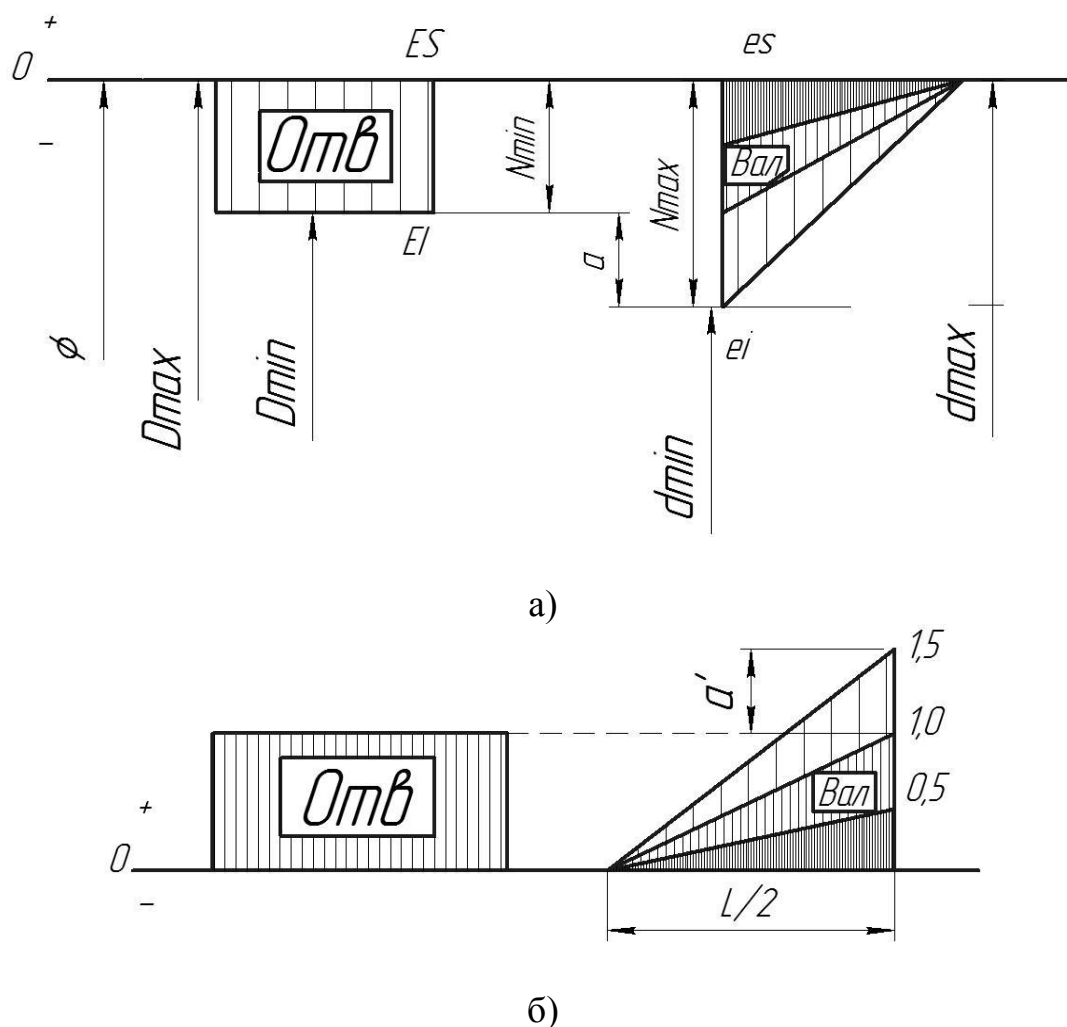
Схема полей допусков для конической пружины:
